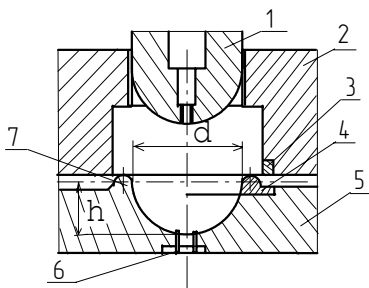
Штмп для сферичного витягування з витяжними ребрами 1-пуансон ; 2-напрямна; 3-вставний притиск; 4-вставне ребро; 5-матриця; 6-виштовхувачі; 7- ребро, виготовлене за одне ціле з матрицею
